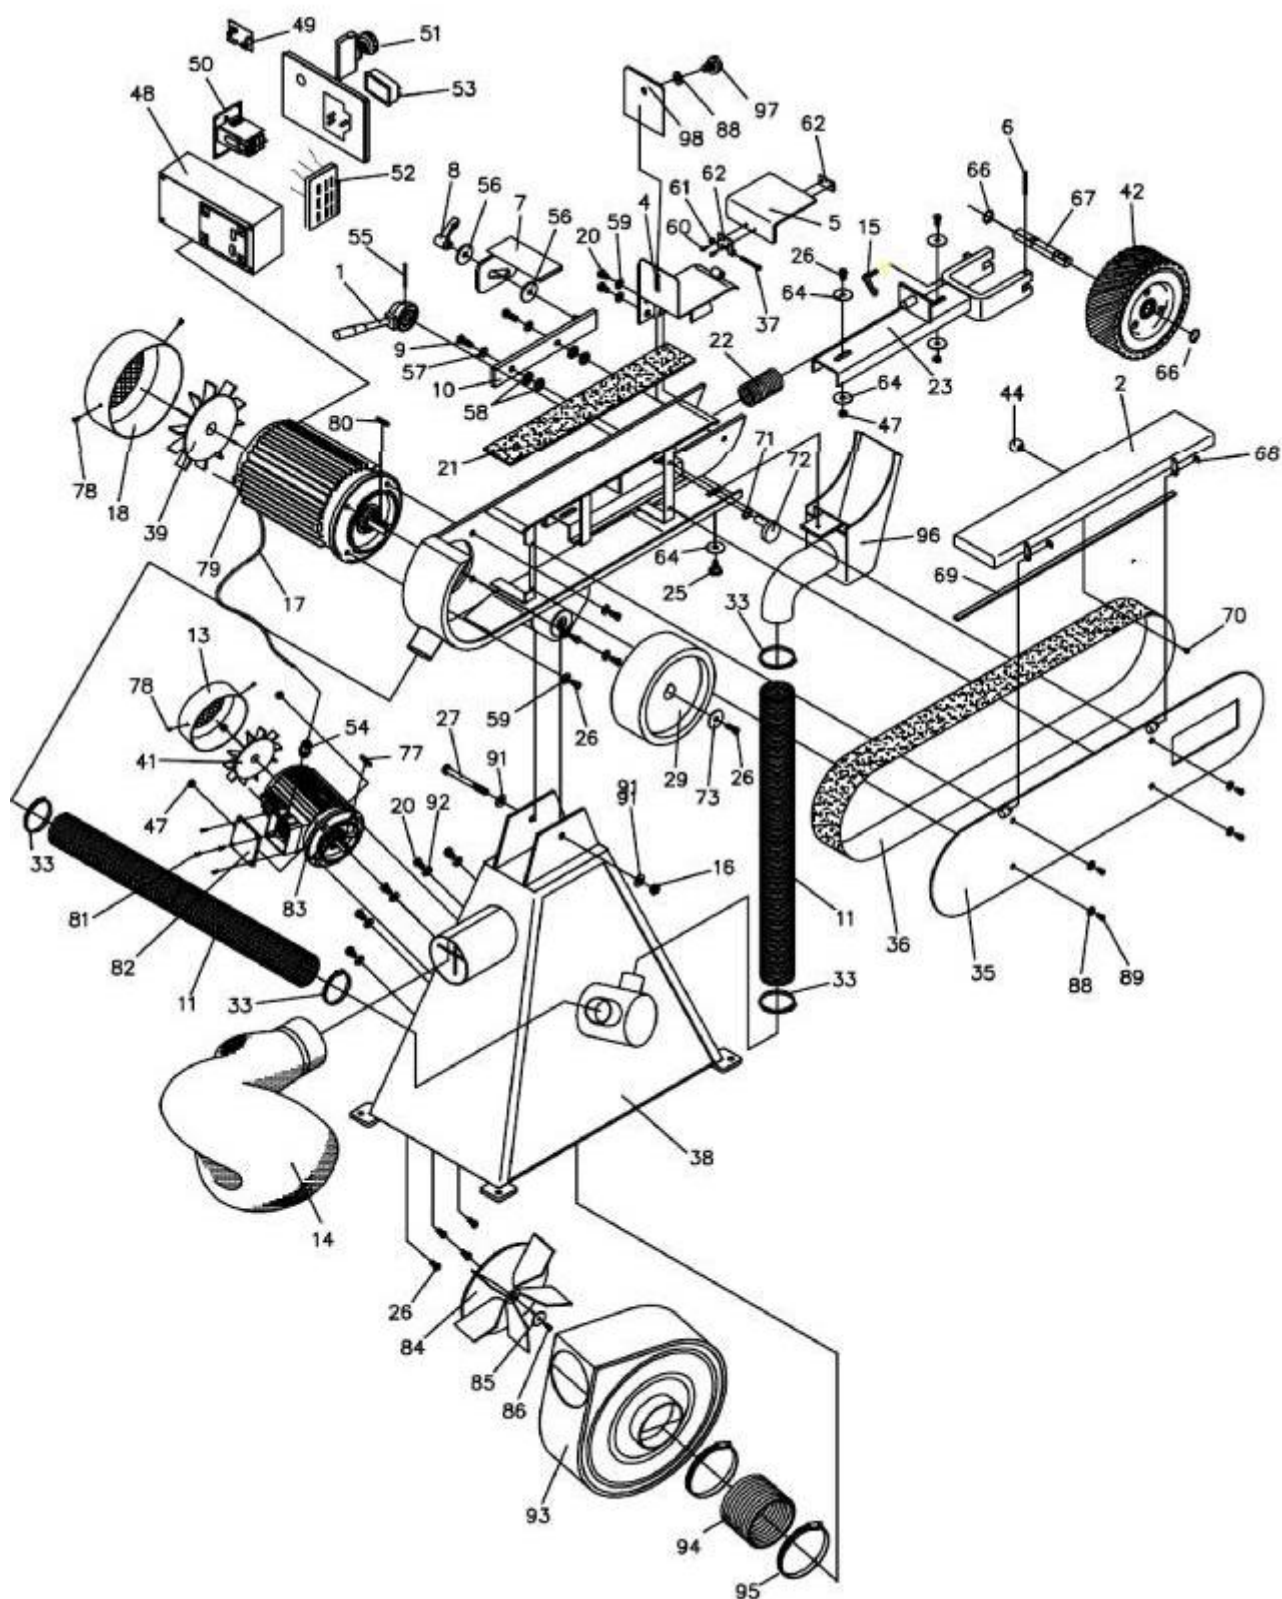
Покомпонентный чертеж ленточно-шлифовального станка с вытяжной системой
